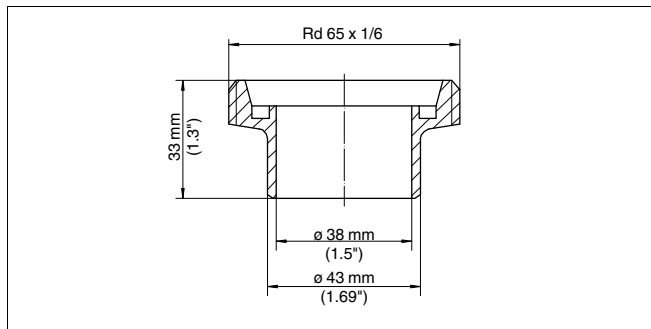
Medidas da luva soldada união roscada para tubo DN 40 conforme DIN 11851
